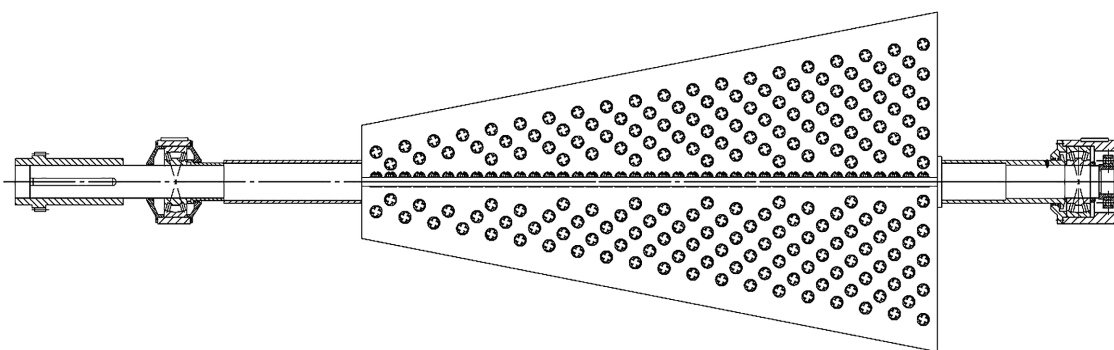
Общий вид вала в сборе роторной части рафинера К-1150/382 с установленными в лопасти конструктивными элементами для дополнительного фибриллирования поверхности древесного волокна
